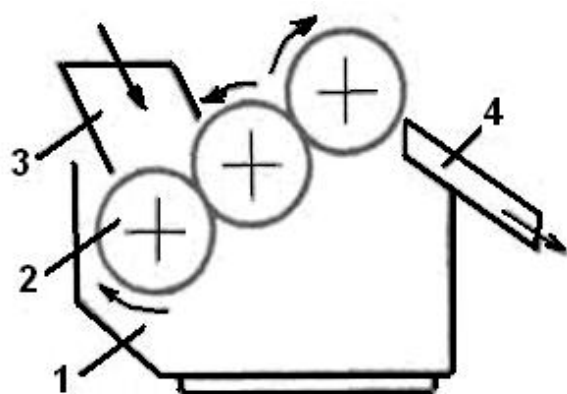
Трехвалковая краскотерка с наклонным расположением валков: 1 – корпус; 2 – валок; 3 - загрузочная воронка; 4 - разгрузочный лоток
